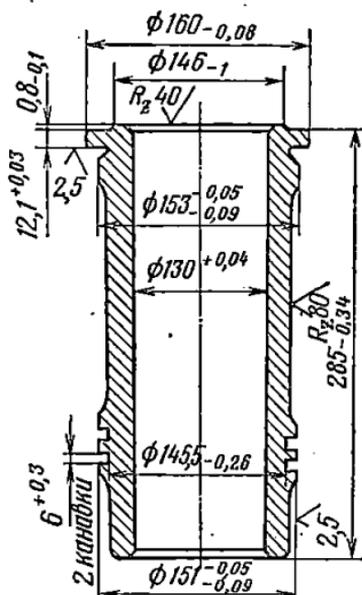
Гильза цилиндра двигателя ЯМЗ-238НБ.
